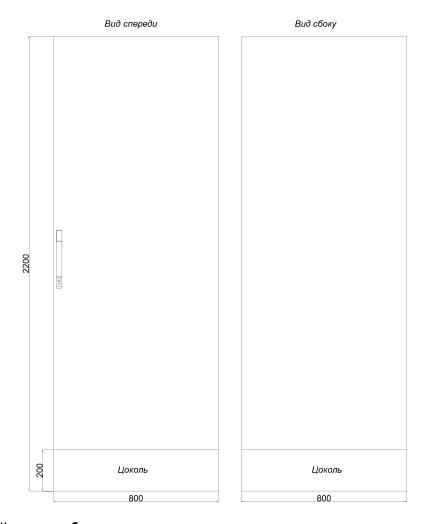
Внешний вид и габаритные размеры концентратора с одностворчатыми дверями
